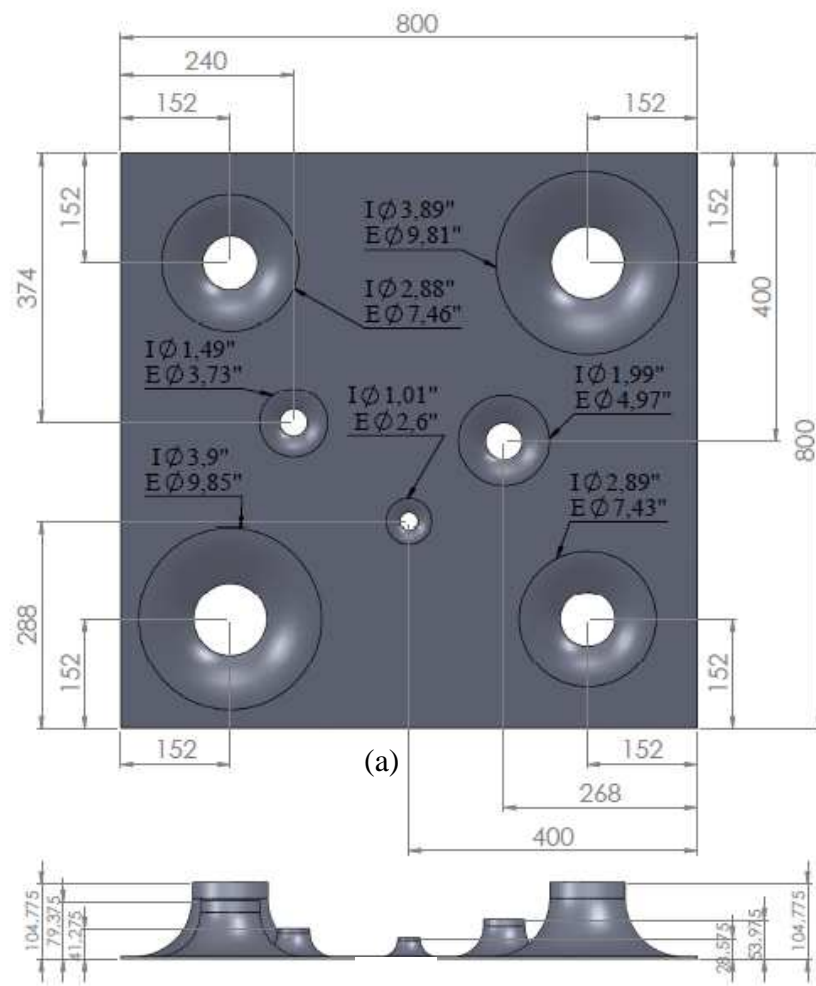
Placa de bocais instalada no interior do túnel. (a) vista frontal; (b) vista superior.
